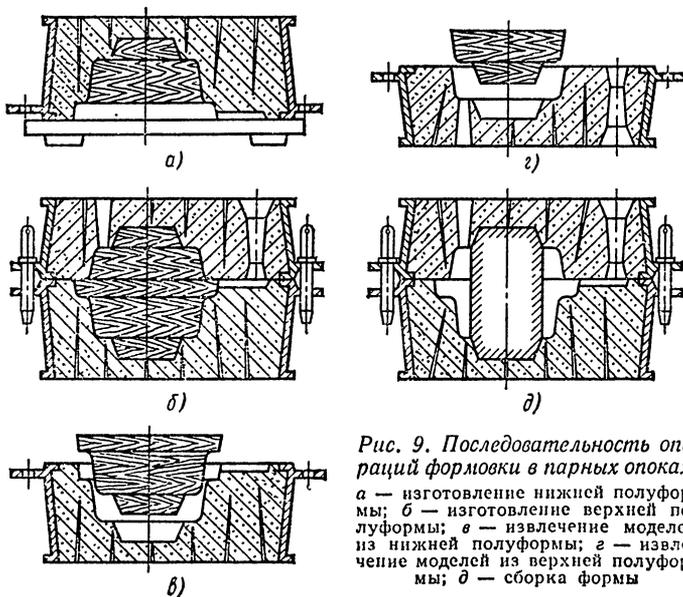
Последовательность операций формовки в парных опоках: а — изготовление нижней полуформы; б — изготовление верхней полуформы; в — извлечение модели из нижней полуформы; г — извлечение модели из верхней полуформы; д — сборка формы
